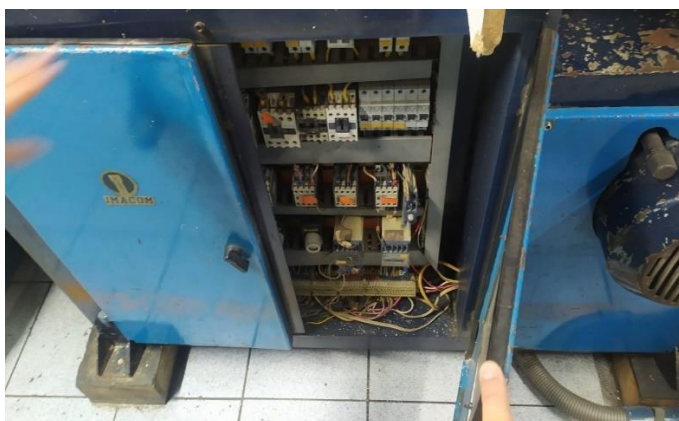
Apertura de puertas del tablero eléctrico para su inspección. Fuente: elaboración propia.
